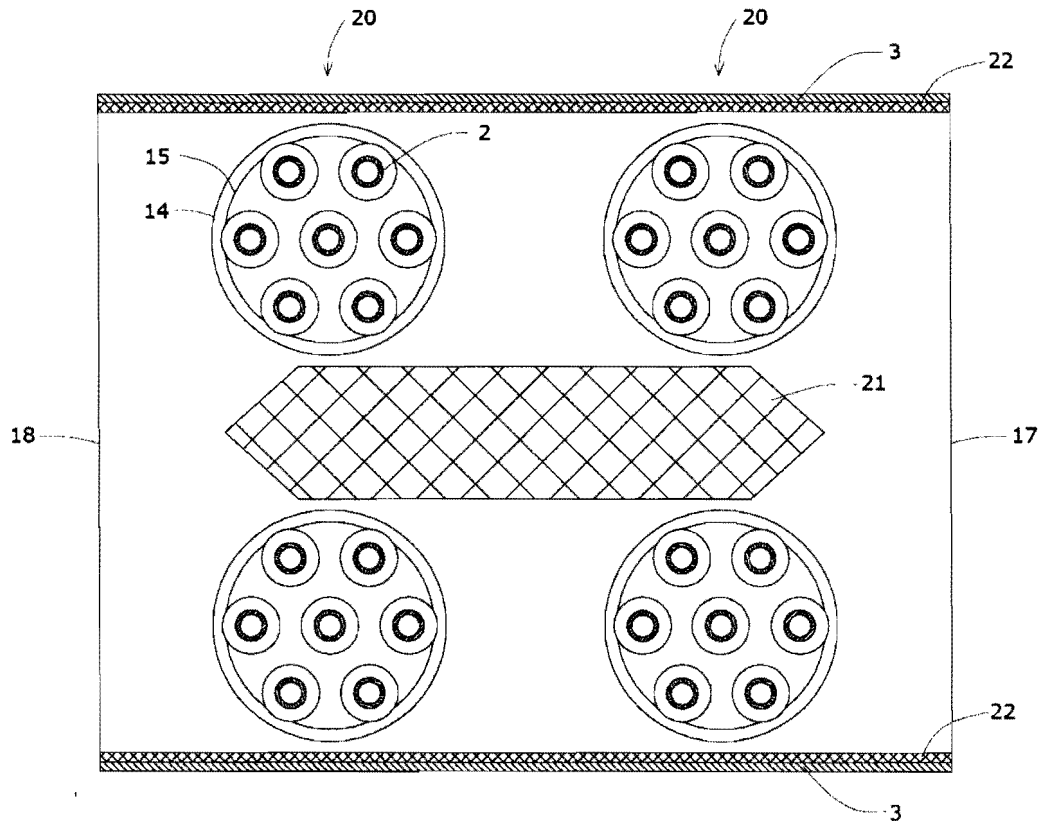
Sectiune orizontala B-B prin schimbatorul de caldura
